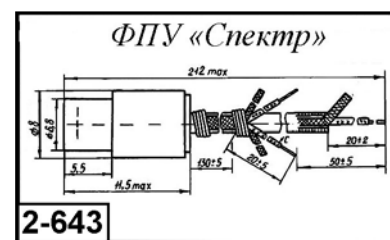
Внешний вид и габаритные размеры ФПУ «Спектр»
